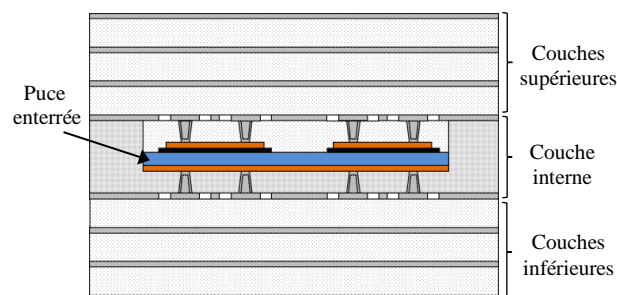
Section en coupe d'un schéma de PWB avec puce enterrée
